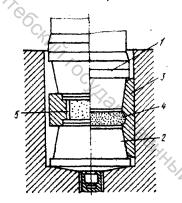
Штамп для заготовок с малым запасом технологической пластичности: 1 - верхний пуансон; 2 - нижний пуансон; 3 кольцевой бандаж; 4 - заготовка; 5 - прокладки
